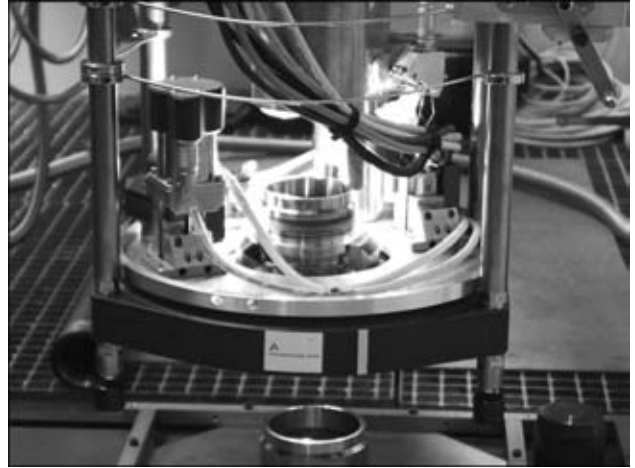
Общий вид планетарной сварочной головки для выполнения кольцевого шва при сварке колпака с патроном
